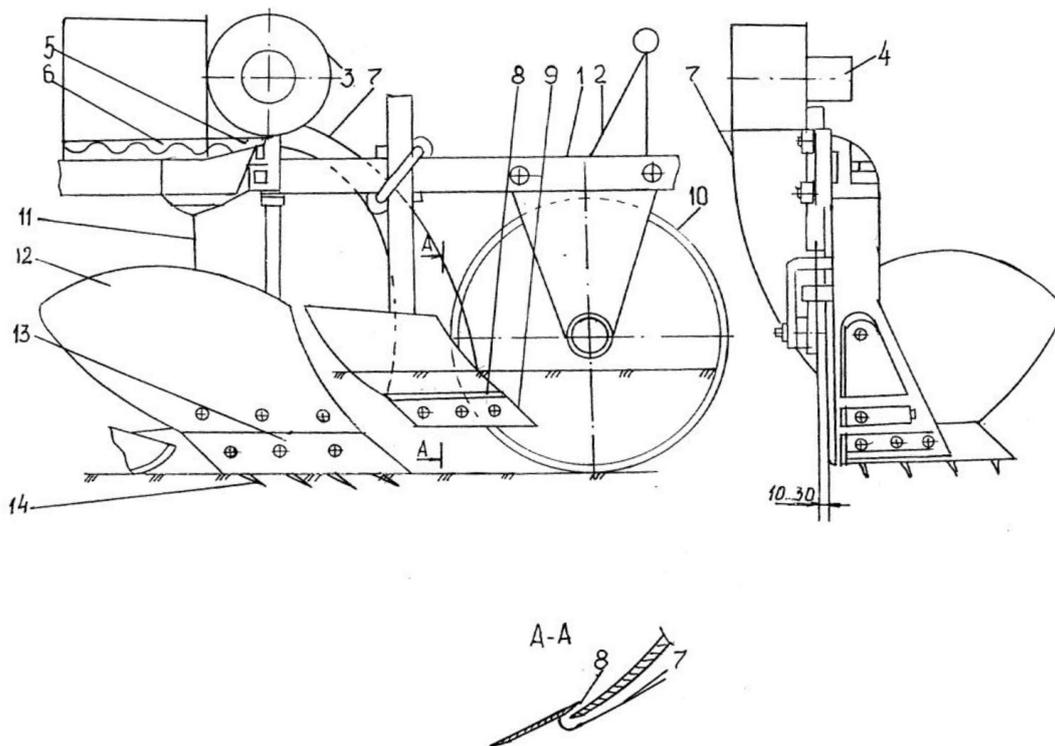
Мелиоративный плуг: 1 – рама; 2 – навесная система; 3 – высоконапорный вентилятор; 4 – гидромотор; 5 – тукопровод; 6 – туковысевающий аппарат; 7 – нагнетательный патрубок; 8 – высеивающее окно; 9 – предплужник; 10 – дисковый нож; 11 – стойка; 12 – отвал; 13 – лемех; 14 – рыхлительные зубья
